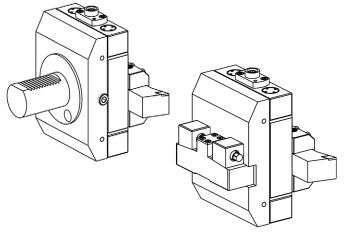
Dynamometer Typ 9129AA mit Maschinenadapter Typ 9129AB40 (links) und Typ 9129AD25 (rechts) und Werkzeughalter Typ 9129AE25
